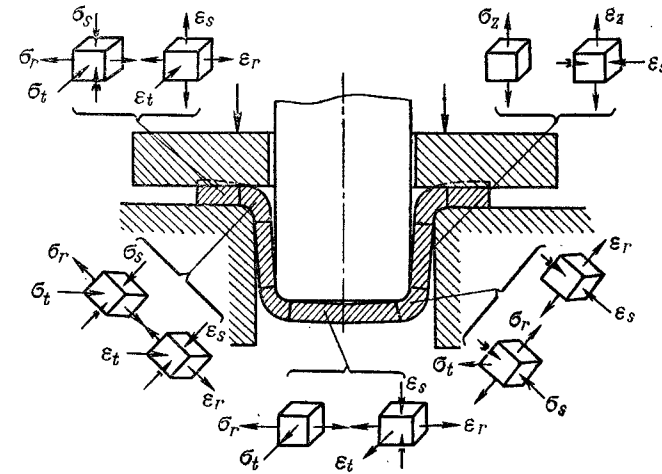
Схемы напряжений и деформаций при вытяжке (σ — напряжения; ϵ — деформации; индексы у σ и ϵ означают: r — радиальные; t — тангенциальные; s — осевые)
